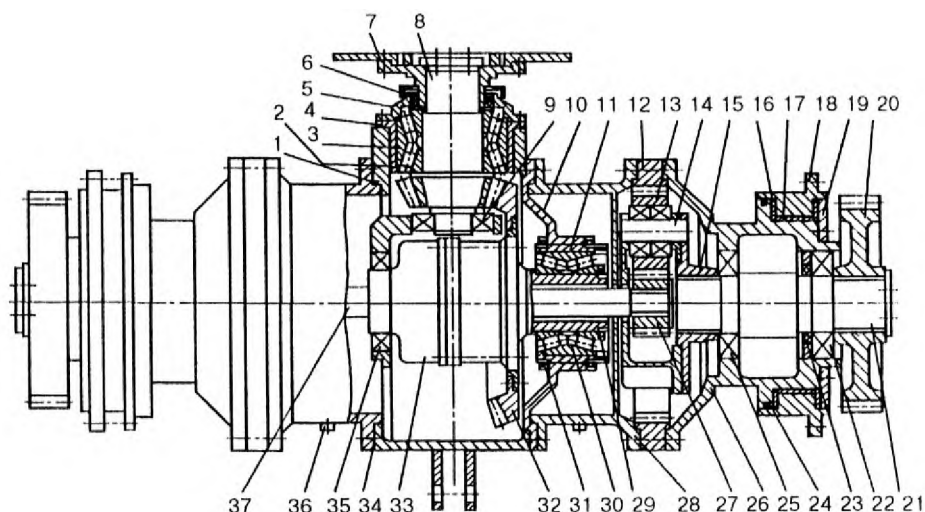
Центральный редуктор моста автогрейдера А120: 1 – корпус; 2, 11 – стаканы; 3, 30 – конические подшипники; 4 – регулировочная прокладка; 5 – крышка; 6, 23 – манжеты; 7, 15, 18 – фланцы; 8 – ведущая шестерня; 9 – роликовый подшипник; 10 – вставка; 12, 13, 20, 27 – шестерни; 14 – ось; 16 – кольцо; 17 – втулка; 19 – диск; 21 – вал; 22, 25, 35 – подшипники; 24 – уплотнение; 26 – ступица; 28 – переходник; 29, 31 – гайки; 32 – ведомая шестерня; 33 – дифференциал; 34 – прокладка; 36 – пробка; 37 – полуось
